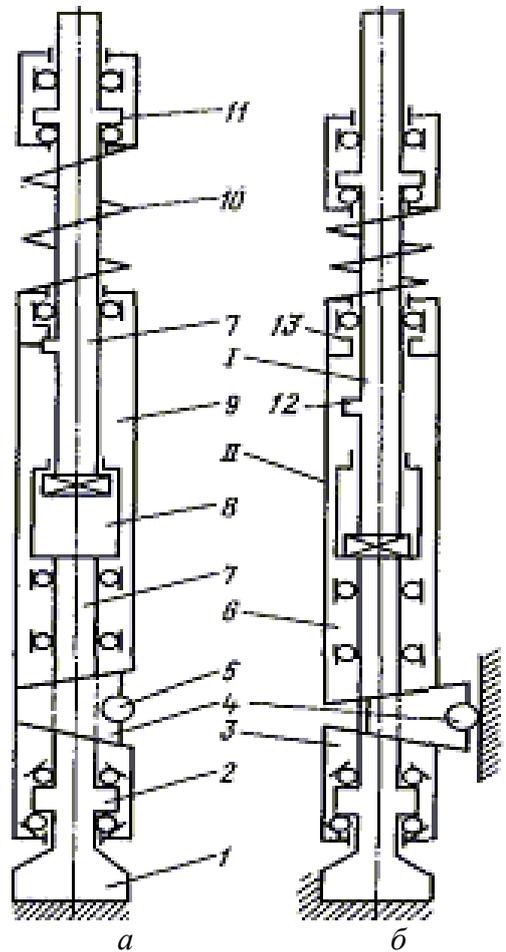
Схема устройства бесклинового постоянно действующего отклонителя ТЗ-3: I – ротор; II – статор; I – долото; 2, II – подшипниковые узлы; 3, 6 – полуклинья; 4 – клин (ползун); 5 – ролик; 7 – валы шпинделя; 8 – муфта шлицевая; 9 – корпус; 10 – пружина; 12 – блокировочный зуб; 13 – муфта; а – при транспортировке, б – при искривлении скважины
